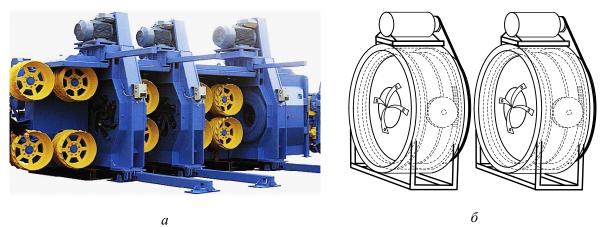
Многороторные станки: a — трехроторный окорочно-оцилиндровочный станок VK-COMBI-3R [1]; δ — принципиальная схема четырехроторного станка
